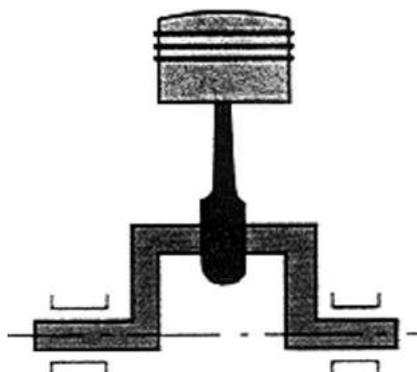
Cambota de motor monocilíndrico com 2 (dois) apoios
